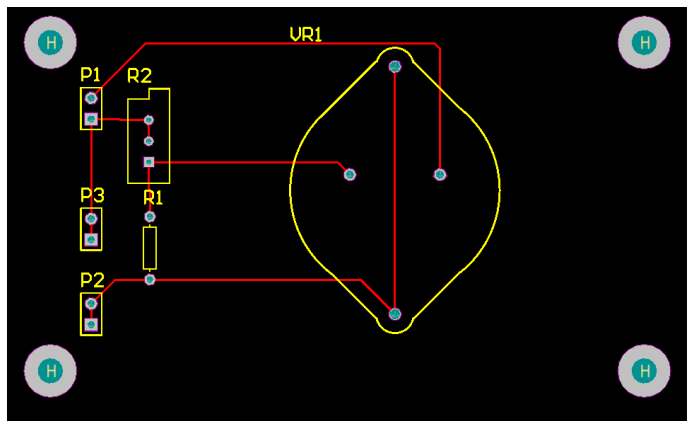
Diseño de PCB de módulo Regulador en Altium Design.
